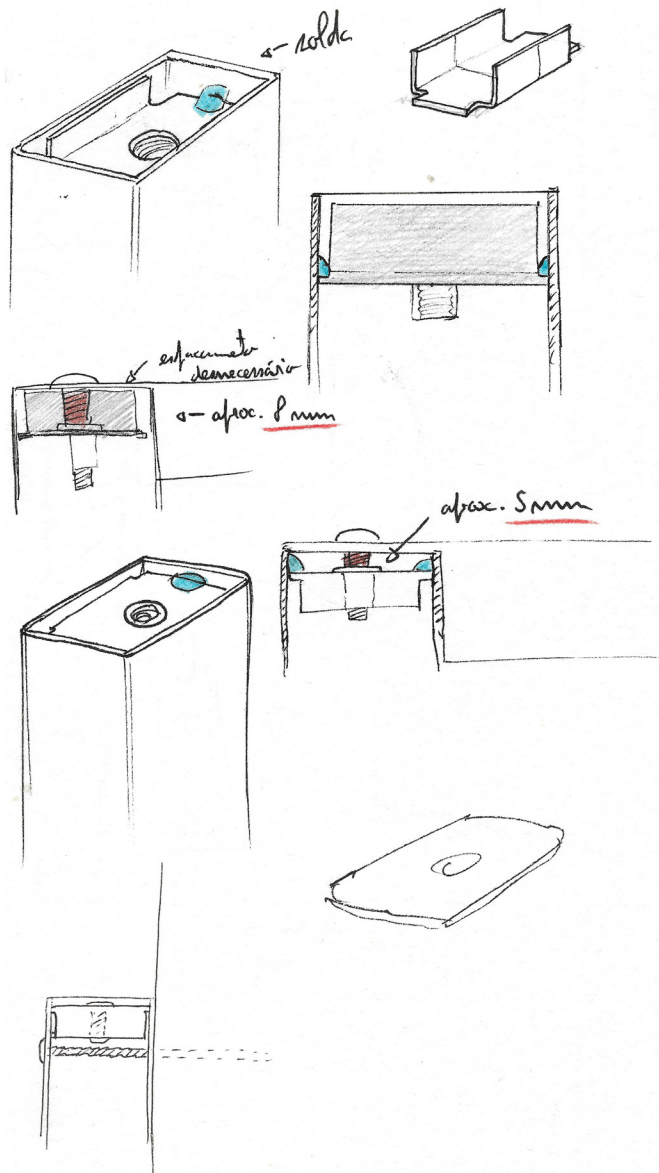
Esboços do detalhe do perfil para aparafusar suporte que distância o perfil da parede
